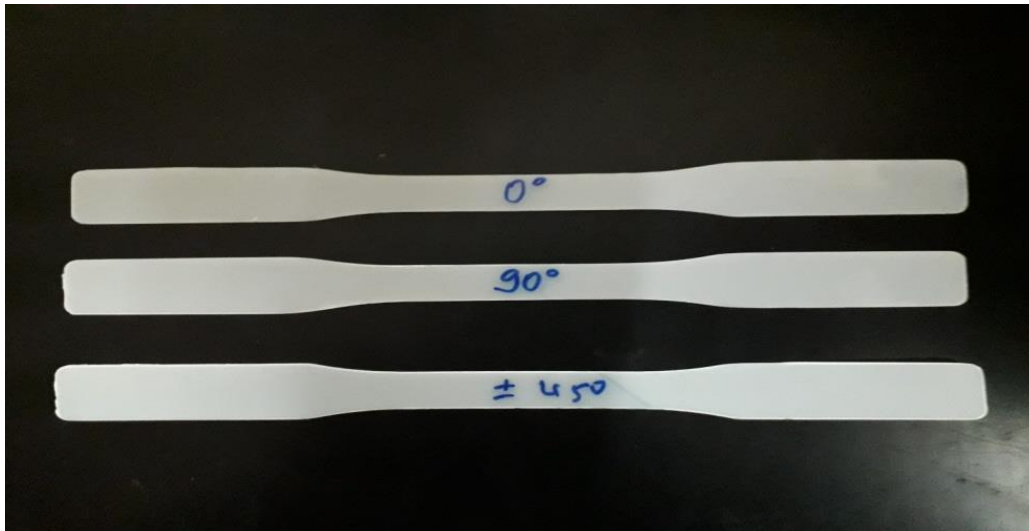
Dimensions des éprouvettes de traction ISO-527 .
